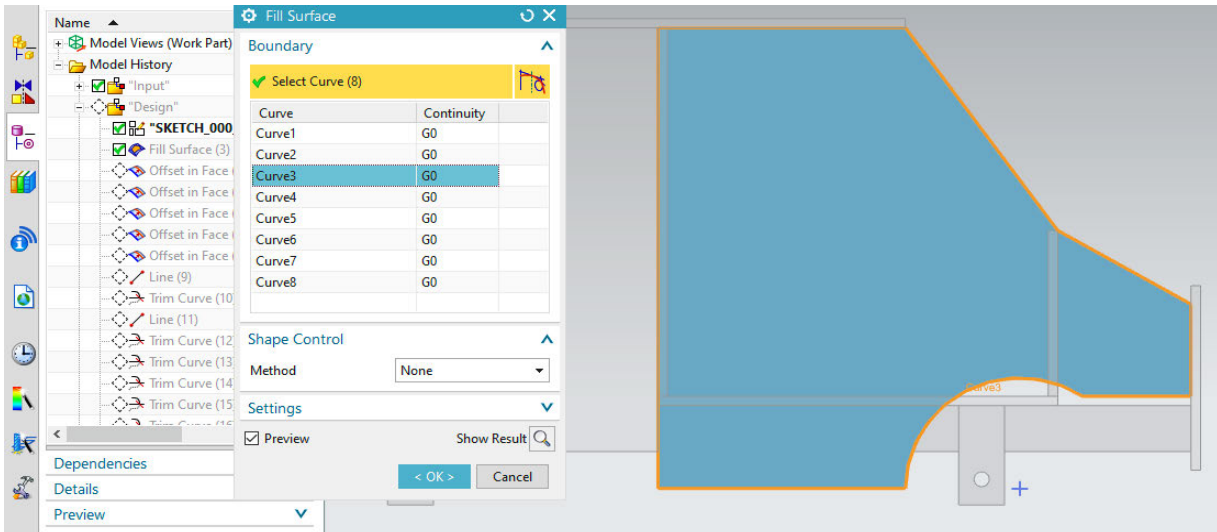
/ Erzeugung der Fläche für die Seitenwände
